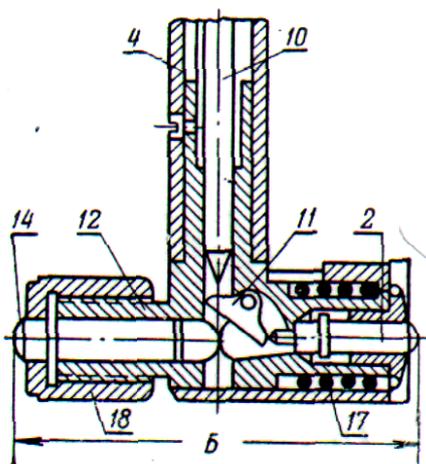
Корпус индикаторного нутромера с рычажной передачей и вставным стержнем: 18 – гайка
